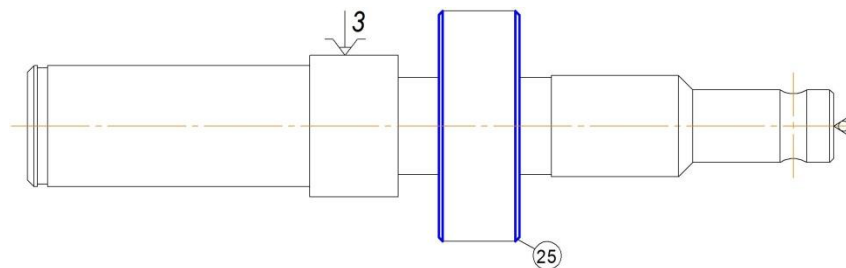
Ескіз обробки деталі на 035 операції.
